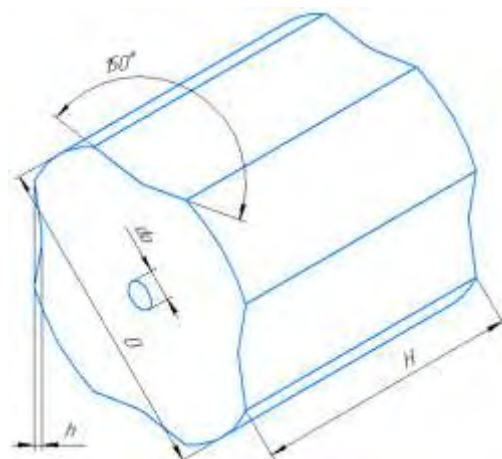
3D-модель профільованої заготовки на чотирипроменевий переріз
